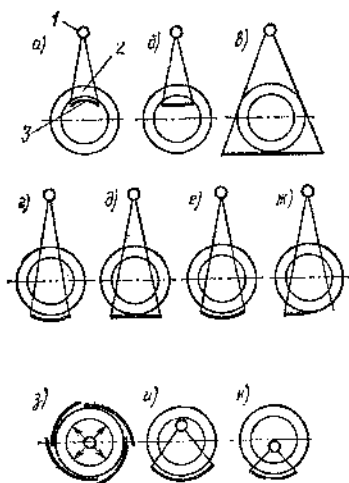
Типовые схемы просвечивания сварных соединений (а—к)
